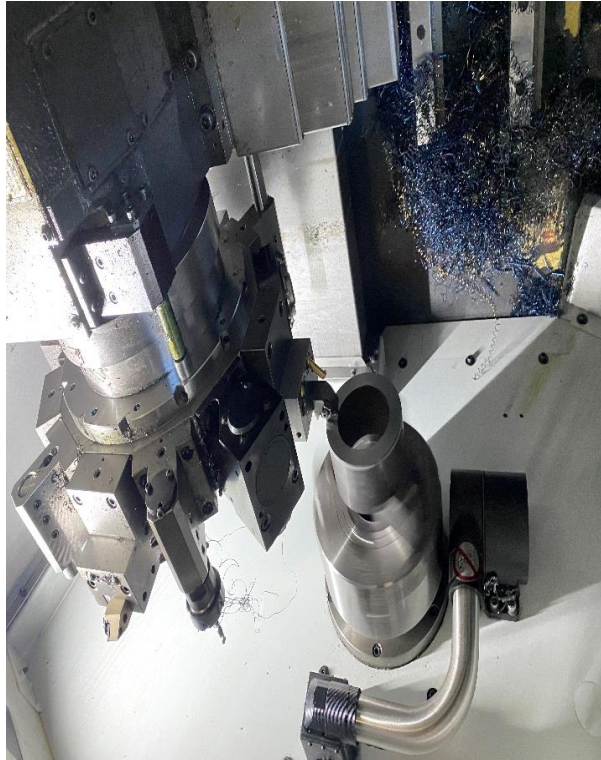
Tubo mecânico já apertado na bucha do Torno CNC
